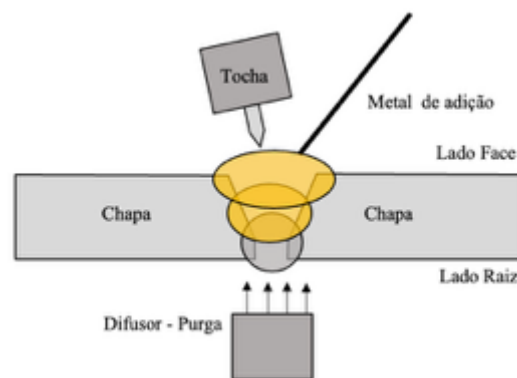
Soldagem do passe de acabamento do CP1A e CP1B no processo GTAW convencional.
